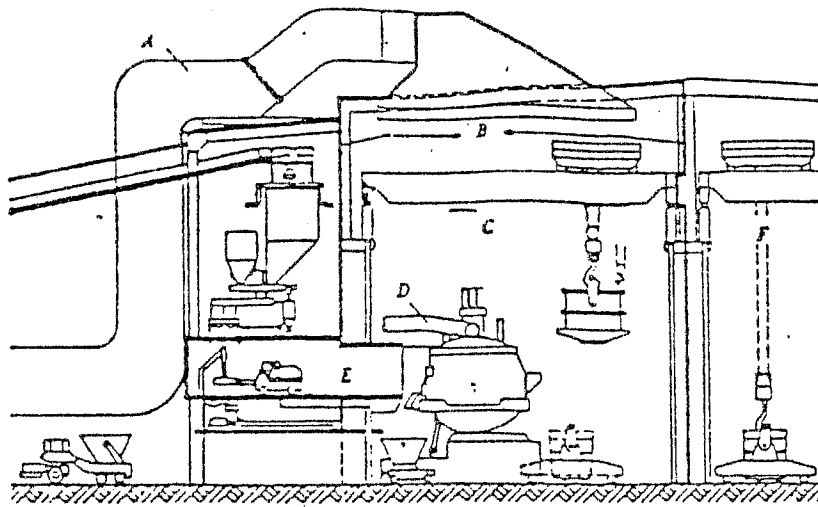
sezione di un'acciaiera elettrica secondo il sistema DEMAG che prevede la separazione della campata forno rispetto alla campata di colaggio e al piano di servizio. A = condotto di aspirazione con cappa; B = pareti di separazione insonorizzanti; C = campata forno; D = aspirazione tramite quarto foro; E = piano di lavoro; F = campata di colaggio .
